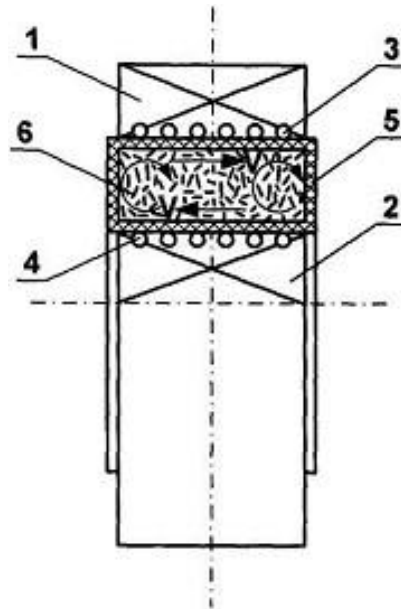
Циліндрична форма активної поверхні індуктора
